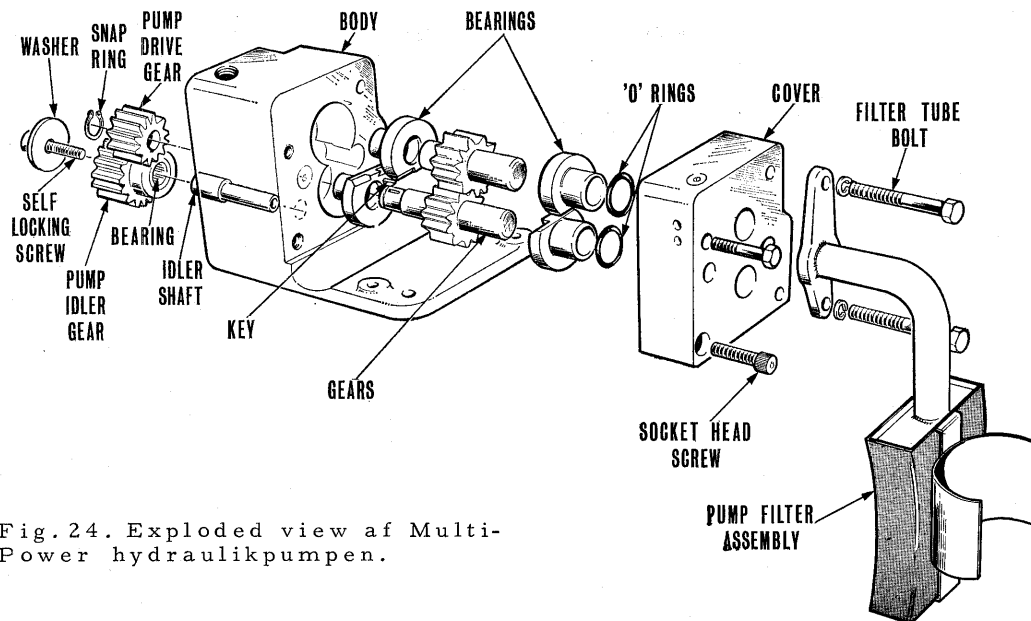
Exploded view af Multi-Power hydraulikpumpen.
